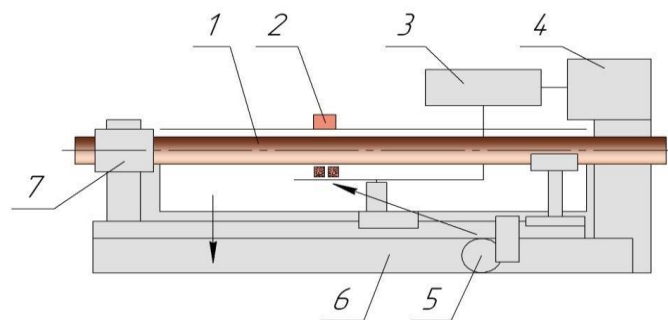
Схема установки для електролітно-плазмової обробки, яка зміцнює, циліндричних виробів типу колінчастий вал (бурова штанга):
